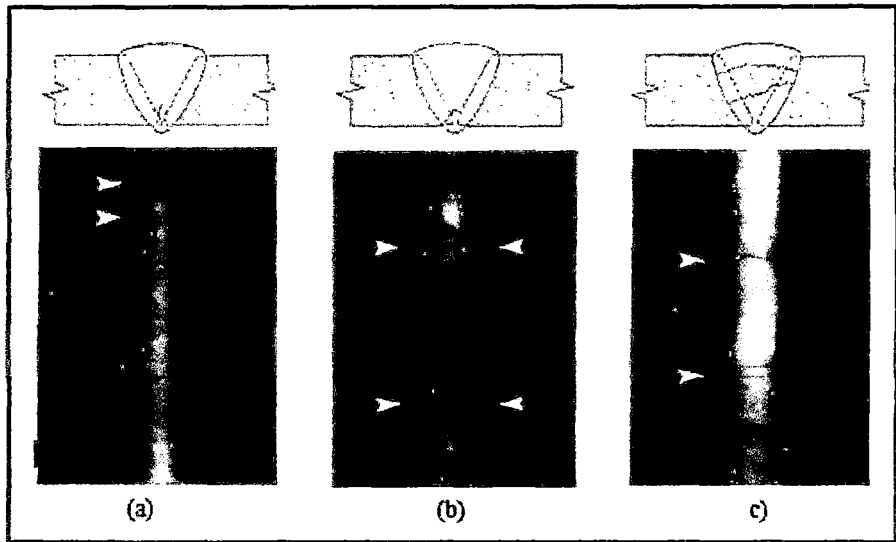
Fisuras en el cordón de soldadura. (a) y (b) fisura longitudinal, (c) fisura transversal.
